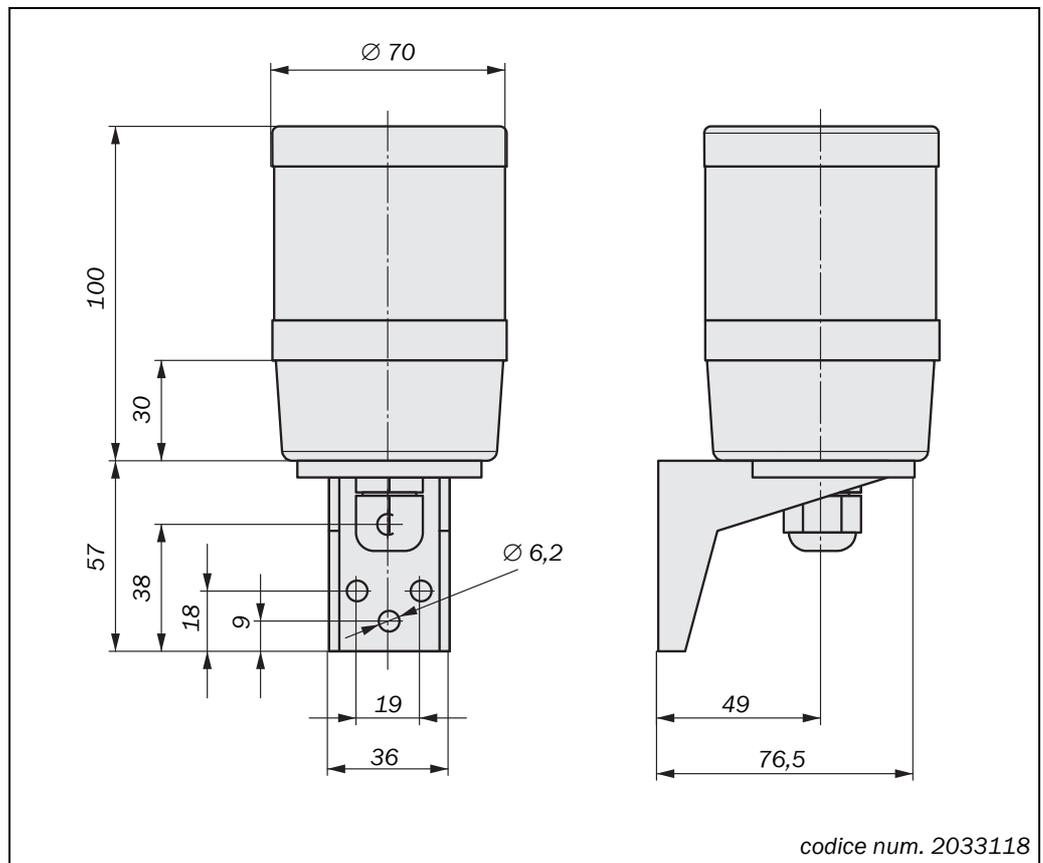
disegno quotato della lampada di inibizione (muting), versione con lampadina (mm)
